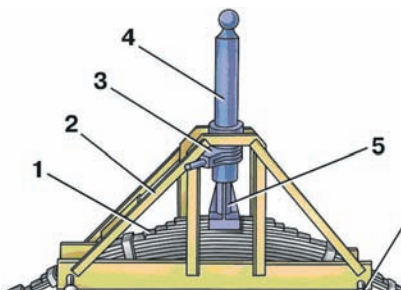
Пристосування для у становки ресор на автомобілях сімейства УАЗ-3741: 1 – ресора; 2 – рама; 3 – важіль; 4 – обойма гвинта; 5 – г оловка; 6 – чека
